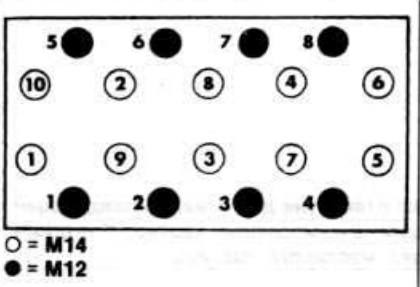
Порядок отворачивания болтов крепления головок цилиндров
